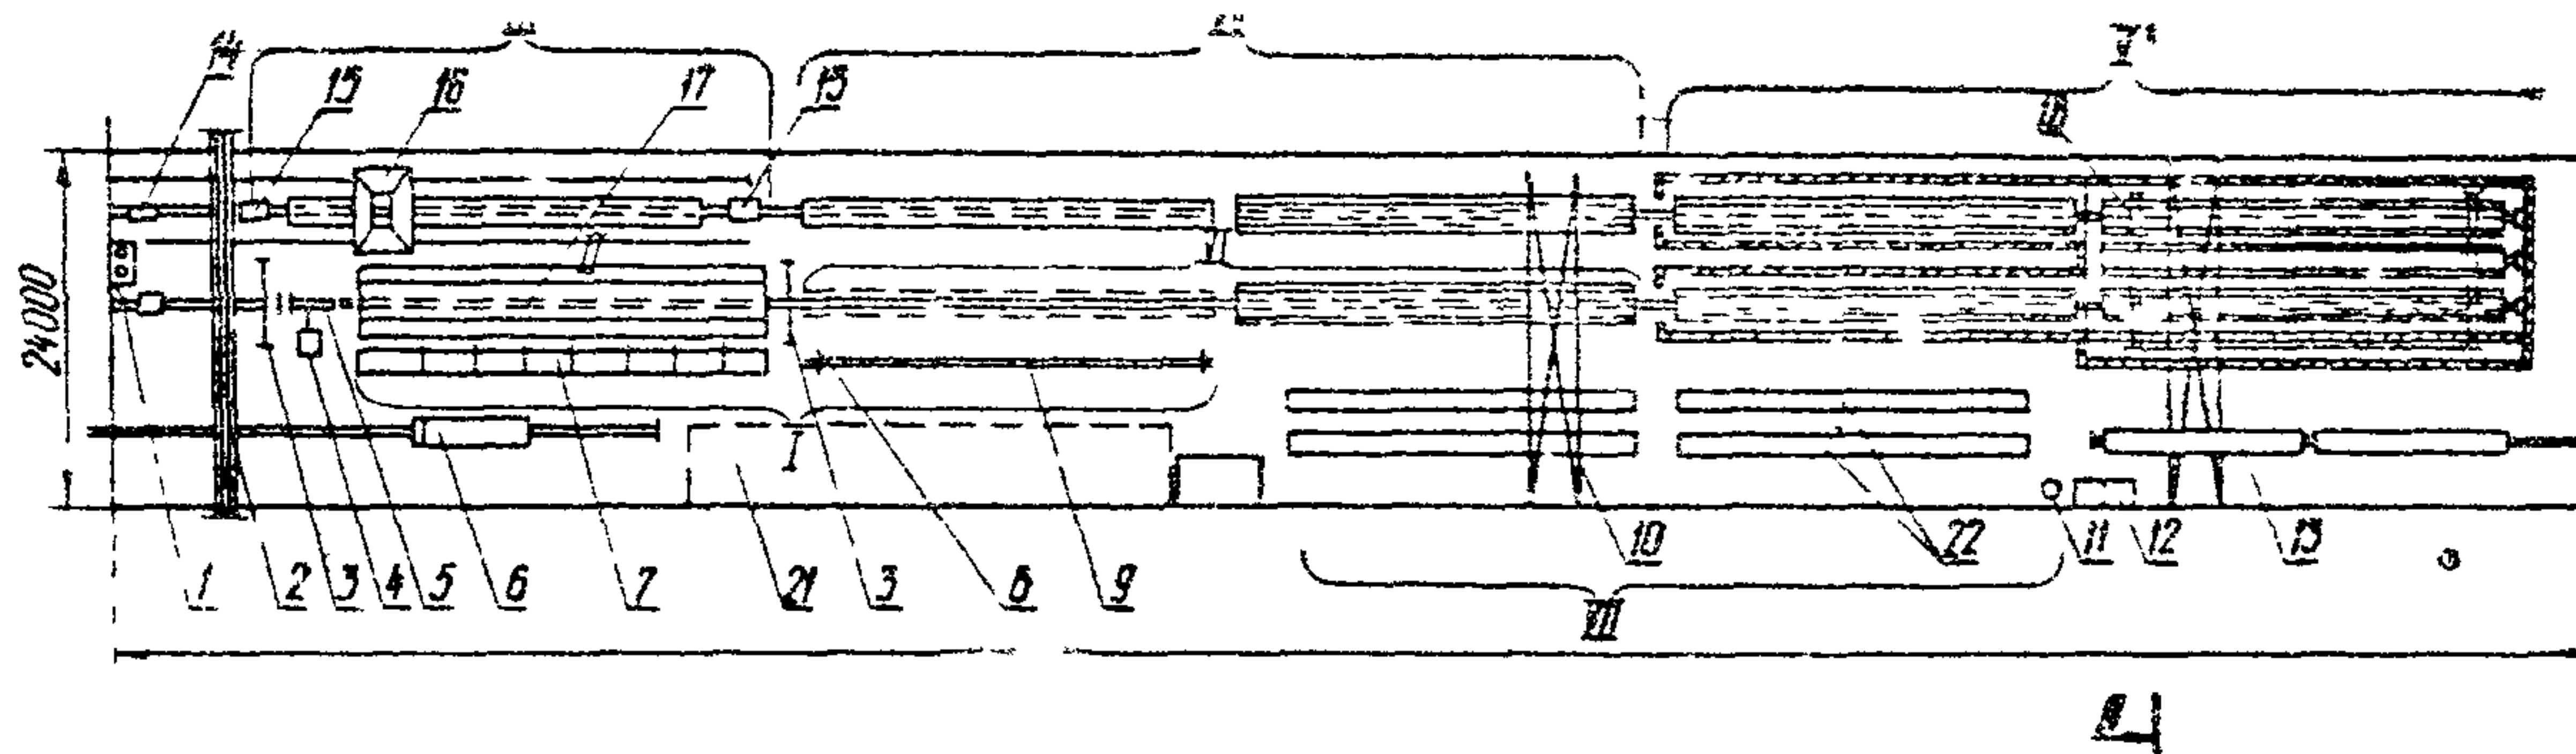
Схема технологической линии: I - супергатор для приготовления смазки; 2 - транспортер подачи бетонной смеси; 3 - защитные экраны; 4 - насосная станция; 5 - гидравлический домкрат; 6 - грузонная тележка грузоподъемностью 5 Т; 7 - станция для сборки арматурного каркаса; 8 - опорные стойки; 9 - траверса для транспортировки арматурного каркаса; 10 - мостовой кран; 11 - бетономешалка; 12 - емкость для материалов; 13 - грузовая тележка; 14 - механизм продольного перемещения; 15 - вибропривод; 16 - бетоноукладчик; 17 - передвижной стенд; 18 - механизм поперечной сдвижки; 19 - пульт управления; 20 - тоннельная камера термовлажностной обработки; 21 - площадка для складирования арматуры; 22 - готовый блок
